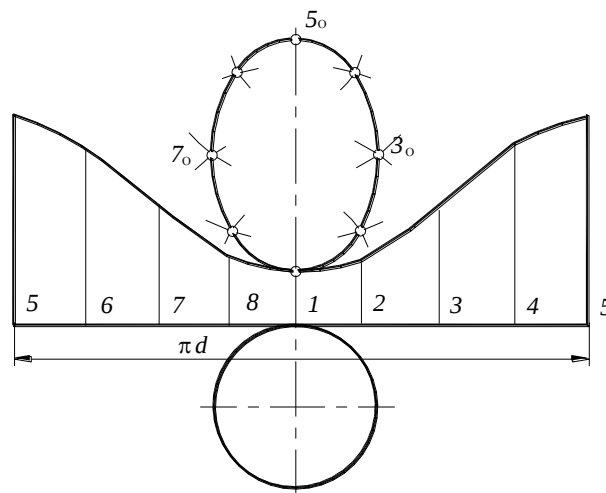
Повна розгортка зрізаної частини поверхні циліндра
